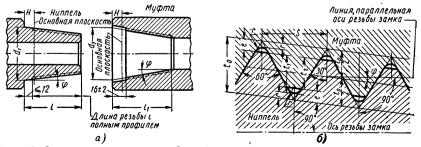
Замковые конические резьбы нефтепромышленности: а — схема соединения; б — профиль резьбы
